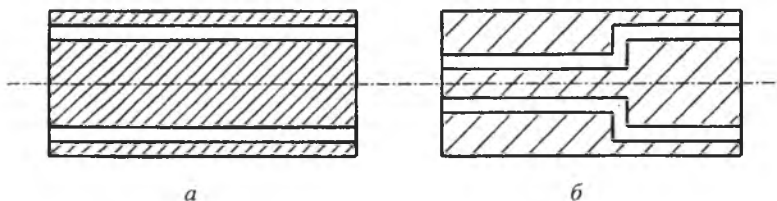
Схема кольцевого сверления: а – сквозное; б – встречное
